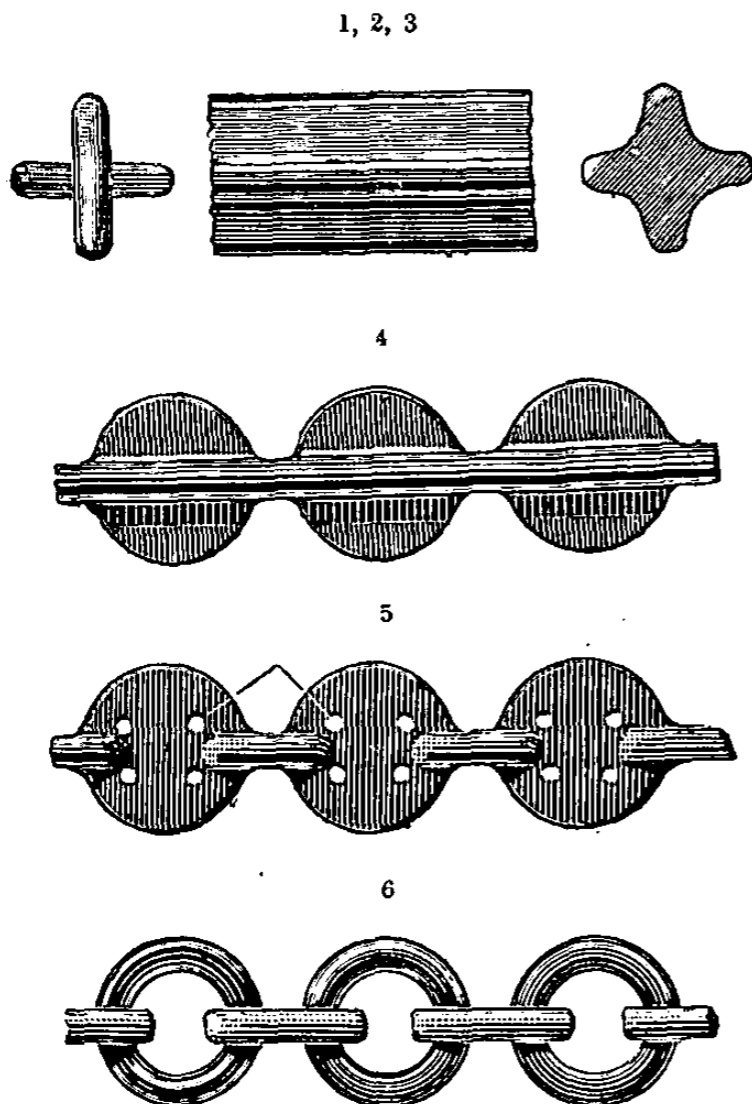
à 327. — Chaîne d'acier sans soudure, procédé Oury.
